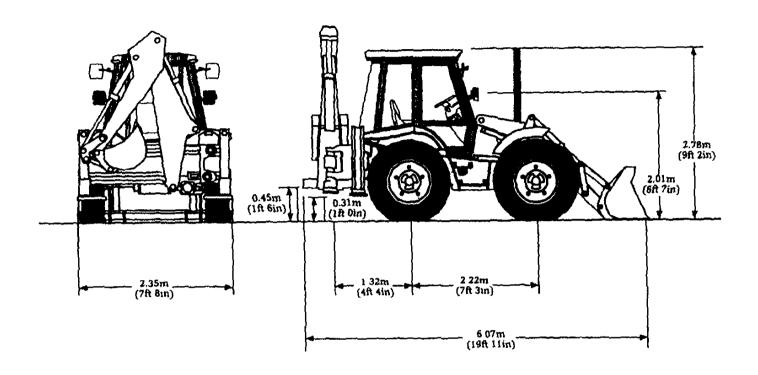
Неполноповоротный экскаватор JCB - 4 CX
